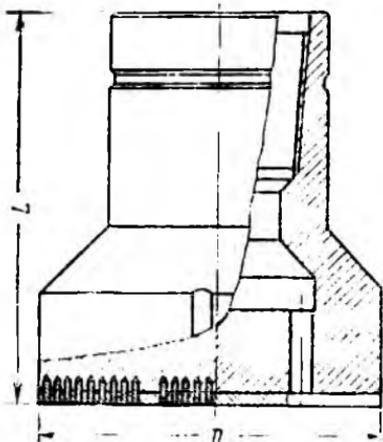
Режуще-истирающий фрезер ФЗ
